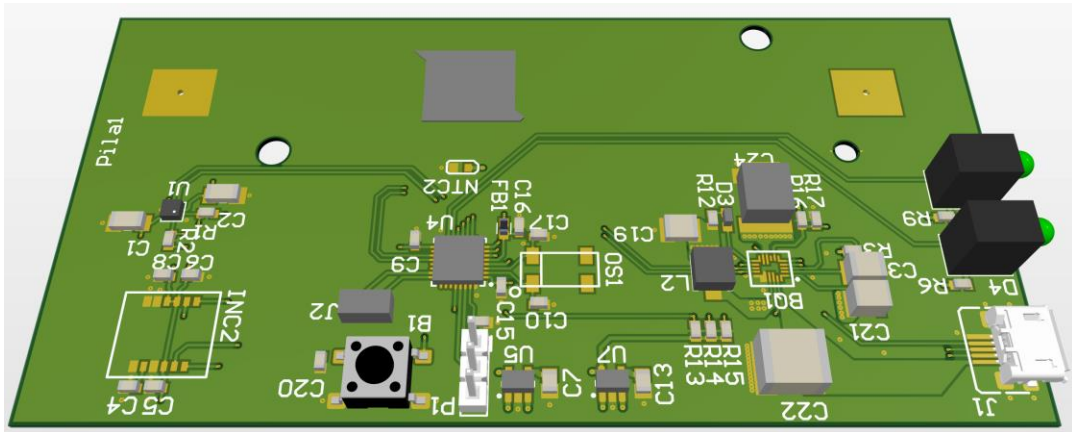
Vista 3D de la tarjeta impresa diseñada.
